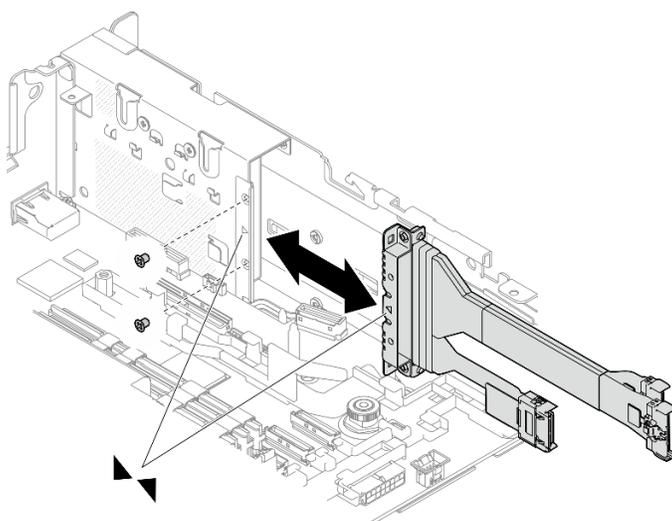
Anbringen des Kabels am OCP-Adapter
